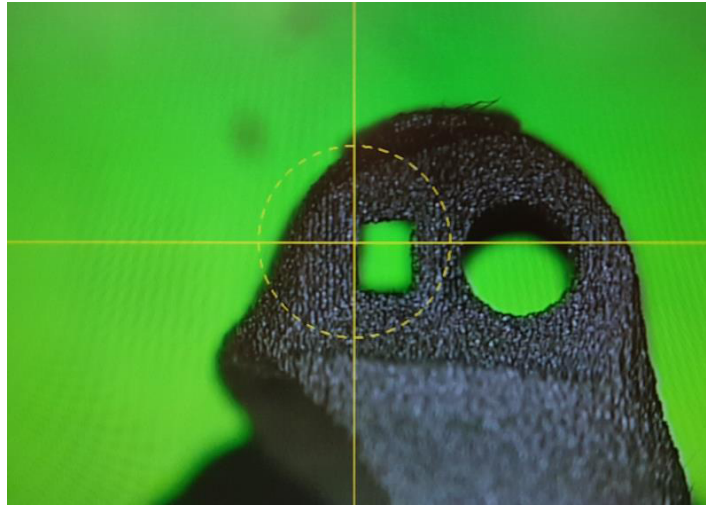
Vue frontale des tubes de bagues personnalisées imprimées en technique SLM (Machine de projection de profil TESA Visio300, grossissement X10)
